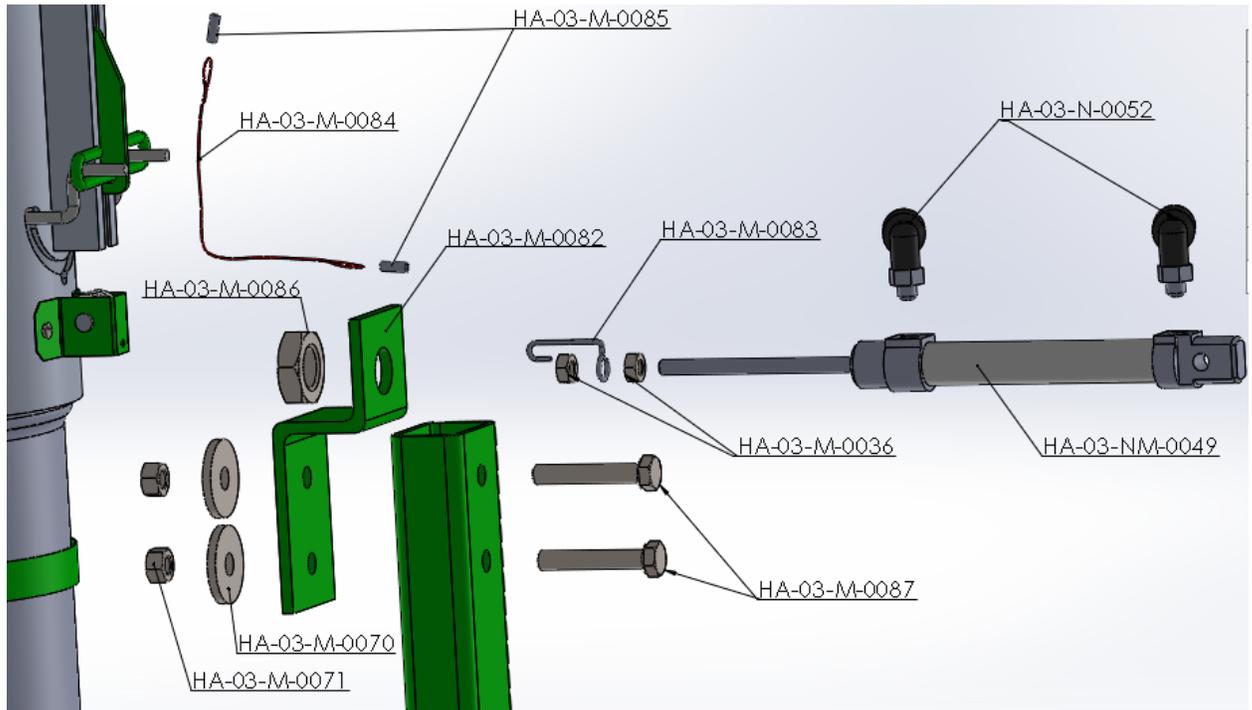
Vista explosionada del sistema de accionamiento de la boquilla 1
